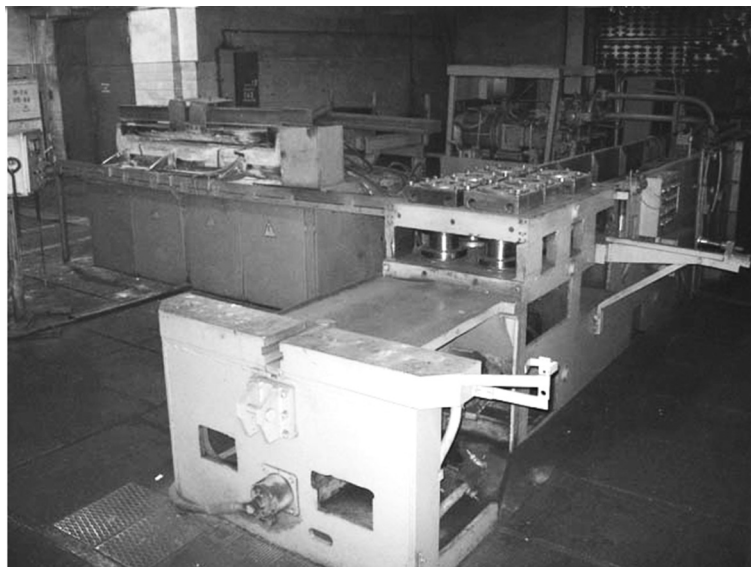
Стан СП-1298М для прокатки заготовок подрессорника
